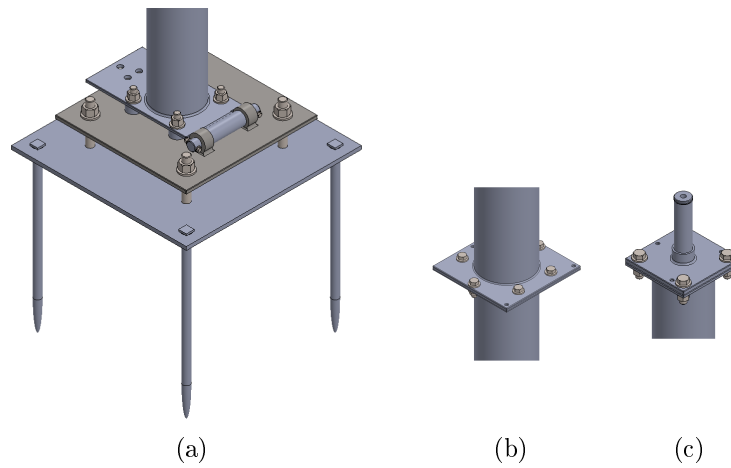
Representação 3D das partes do poste: (a) sapata; (b) união dos tubos; (c) fixação da turbina.
